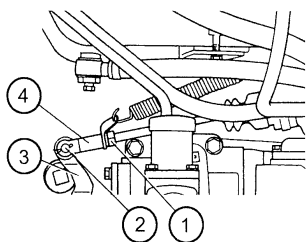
Регулировка механизма управления сцеплением: 1 – контргайка; 2 – палец; 3 – рычаг; 4 –вилка
